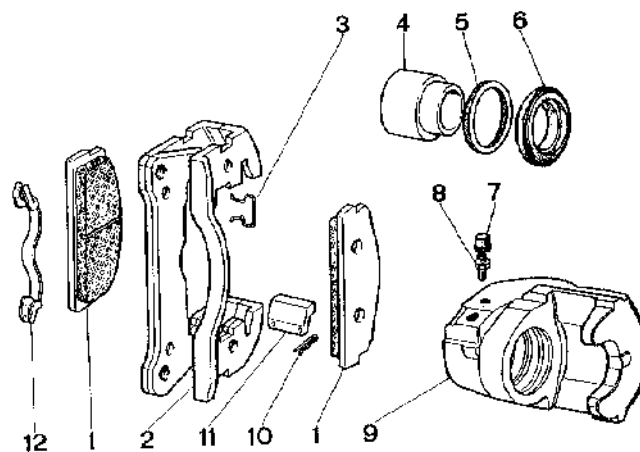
Vue éclatée d'un étrier de frein AV et de sa chape.
